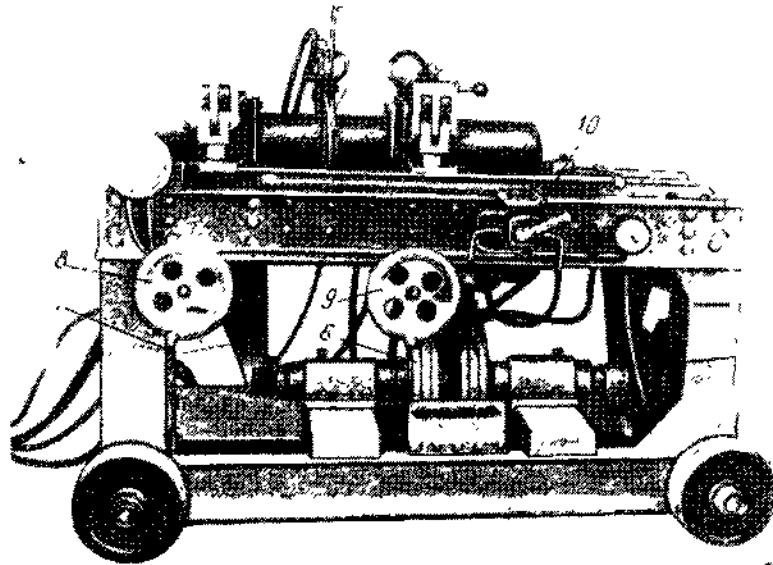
Станок МГСП 15/160-53 для газопрессовой сварки
